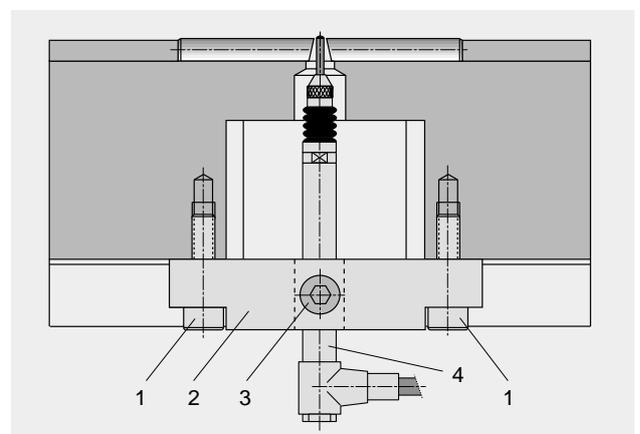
Zwei Schrauben (1) befestigen den Tasterhalter (2) am Messtisch; Klemmschraube (3) für den Messtaster B (4)
